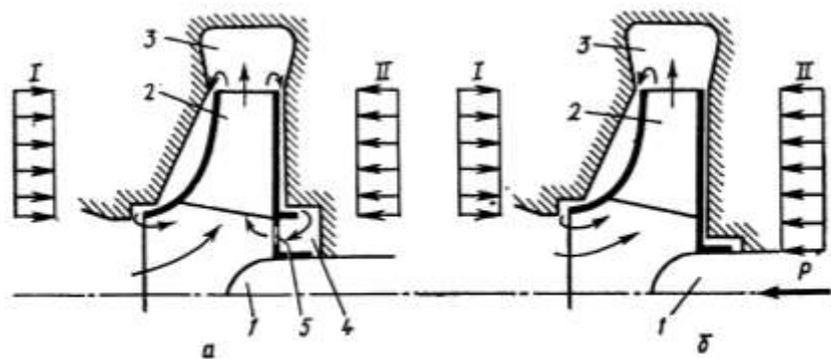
Схемы рабочих колес: а — с разгрузочной камерой; б — без разгрузочной камеры; 1 — вал; 2 — рабочее колесо; 3 — спиральный отвод; 4, 5 — разгрузочная камера и отверстие; I, II — опоры статического давления на левый и правый диски
